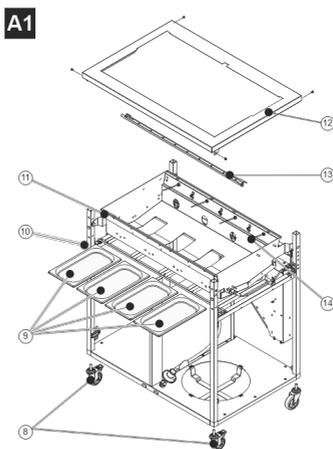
Vue d'ensemble groupe « A » (A1, vue avant)
